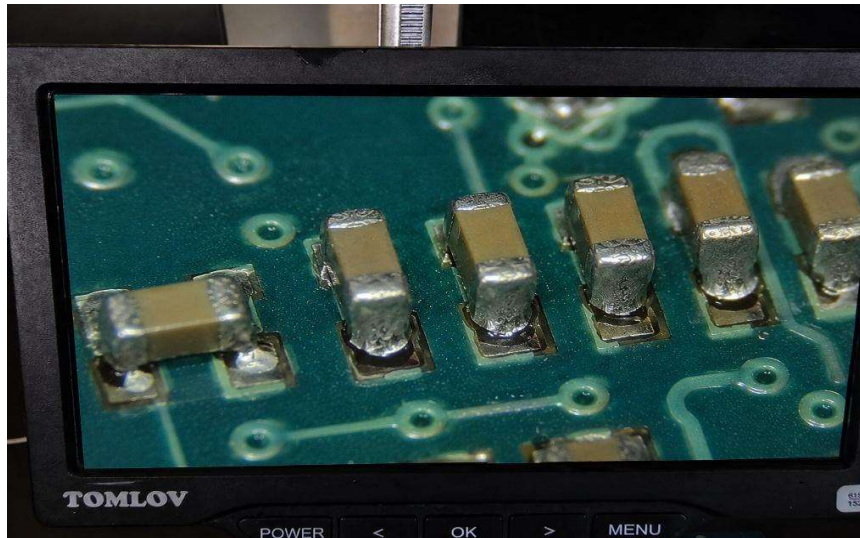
Imagen vista desde microscopio (defecto insuficiencia de soldadura).
